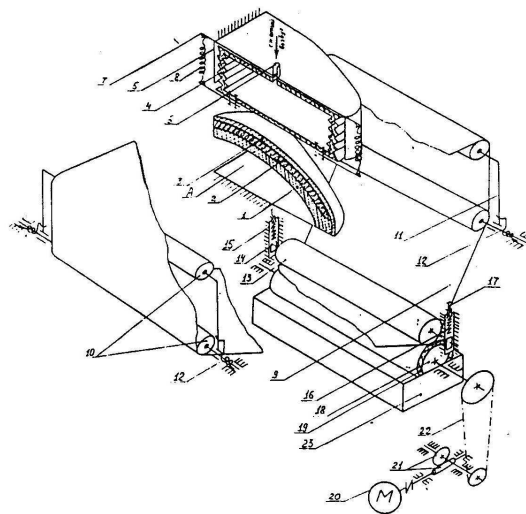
Устройство для увлажнения носочно-пучковой части заготовки верха обуви
